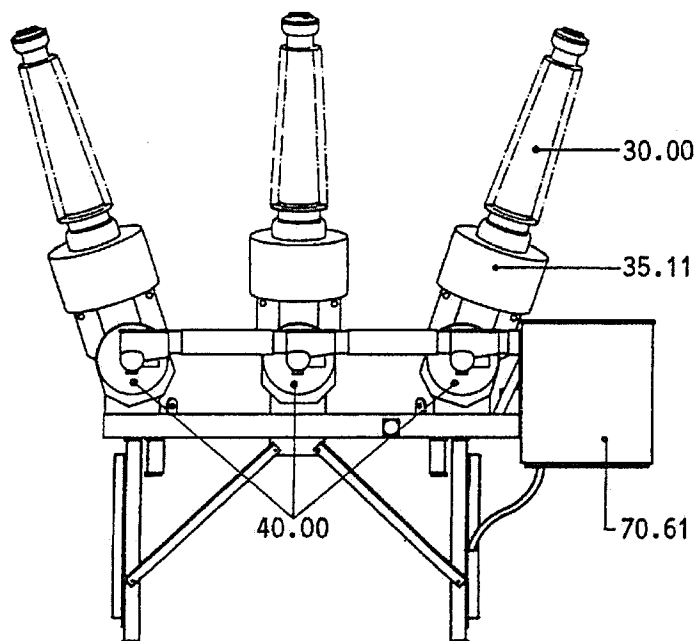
А: Общий вид выключателя (вид со стороны картеров и механической связи между полюсами и Приводом)
